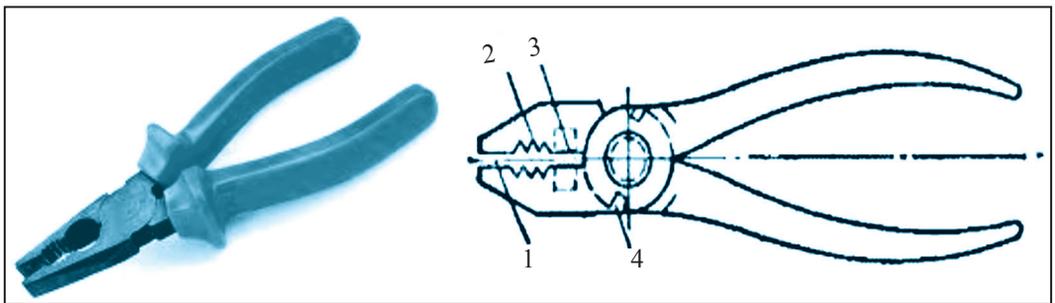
Плоскогубцы: 1 – плоская сдавливающая часть; 2 – дуго-видная часть, предназначенная для прочного удержания предметов цилиндрической формы; 3 – режущие лезвия; 4 – маленькое углубление для резки проволоки с круглым сечением.
